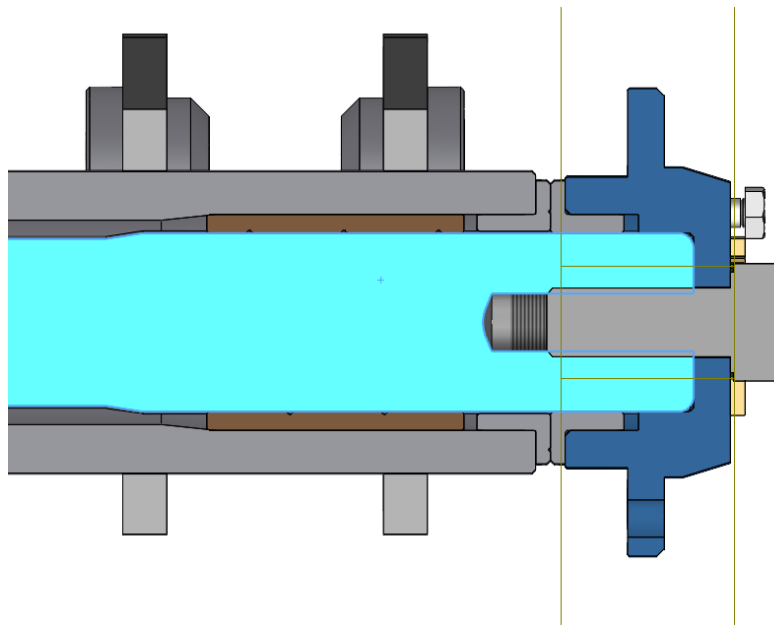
Ajustamento entre apoio da cavilha e cavilha.
